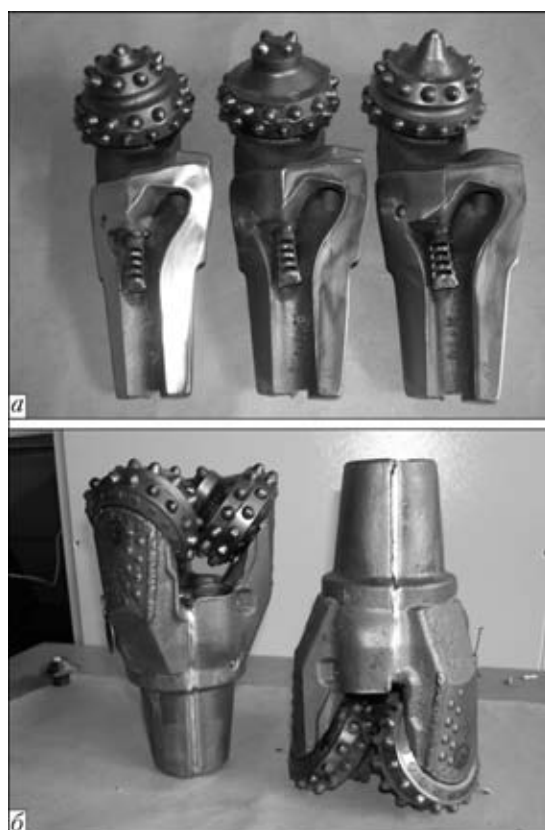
Внешний вид трех элементов долота до сборки и сварки (а) и сваренного электронным пучком долота (б)
